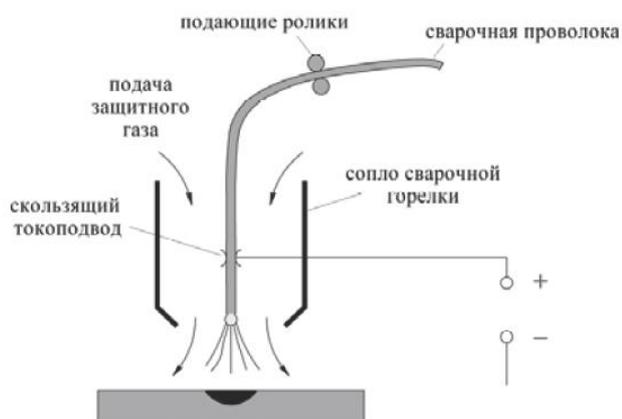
Механизированная сварка в защитном газе
